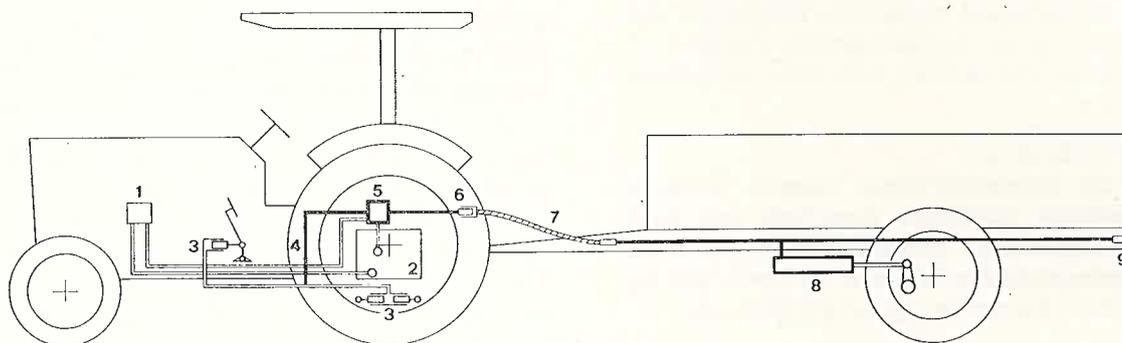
Hydraulische Anhängerbremse, Bedienung mit dem Bremspedal des Traktors und Ansteuerung durch die hydraulische Traktorbremse.
